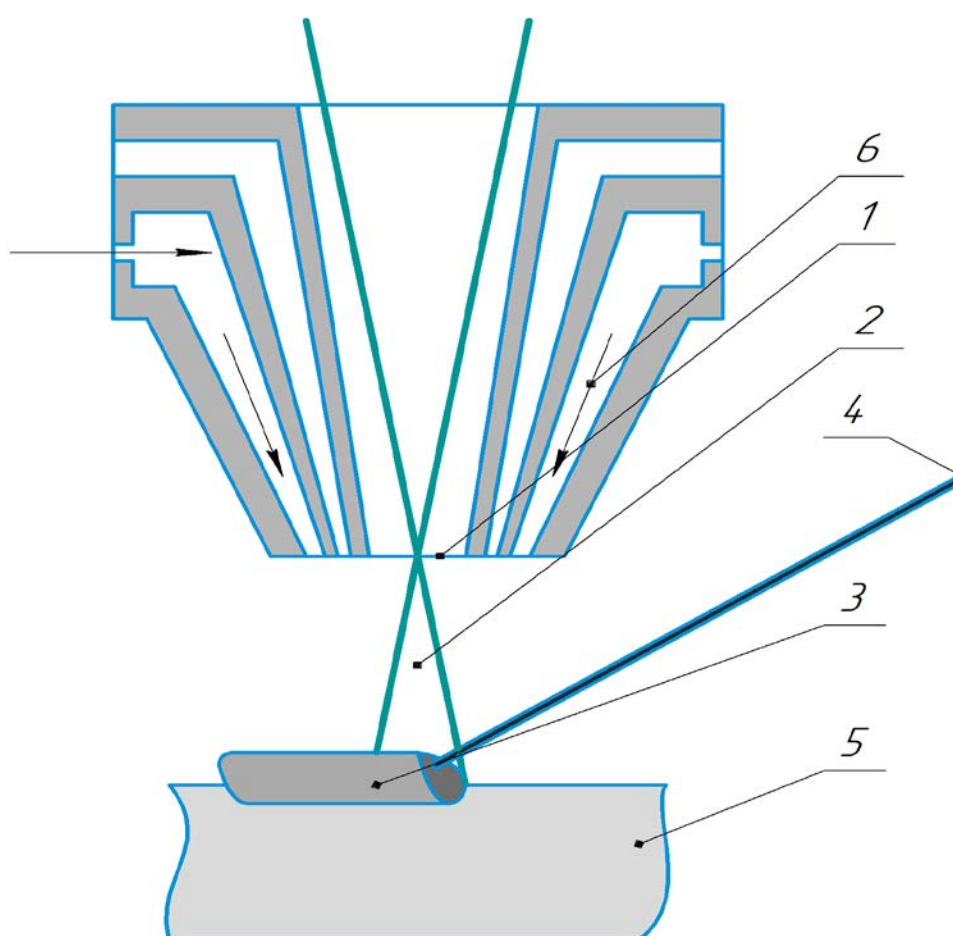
Схема процесса лазерной наплавки с подачей присадочной проволоки: 1. Защитное стекло объектива. 2. Лазерное излучение. 3. Наплавленный материал. 4. Присадочная проволока. 5. Деталь. 6. Защитный газ
